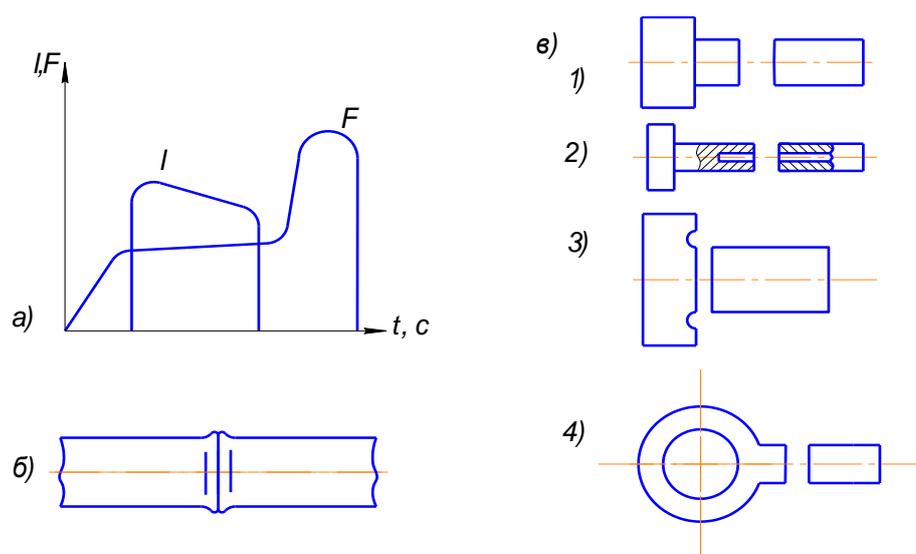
Схема контактной стыковой сварки сопротивлением:
